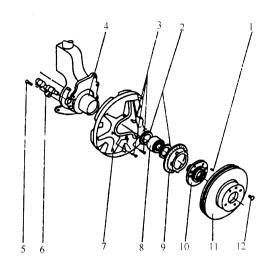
前轮轮速传感器和 前轮轴承的安装位置
